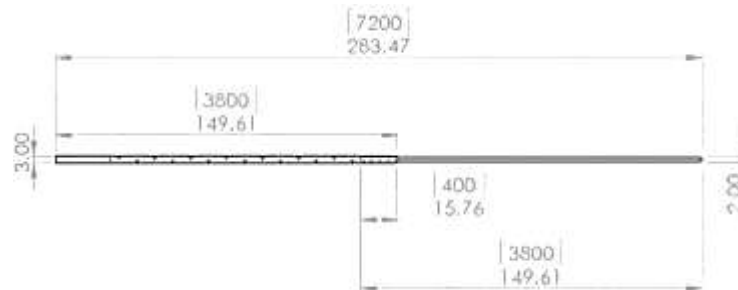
Dimensiones principales de la grúa a construir; pulgadas, [mm].
